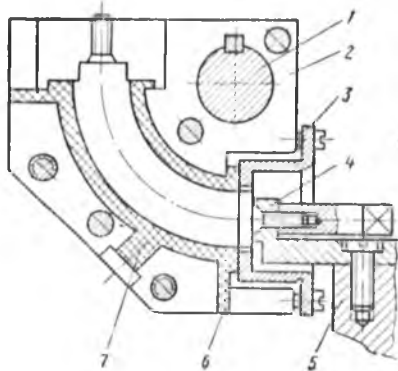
Приспособление для извлечения формы из плавного волноводного изгиба:
